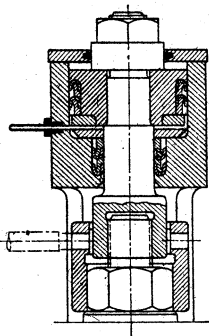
Preßöl-Vorspannpresse für große Schrauben.
